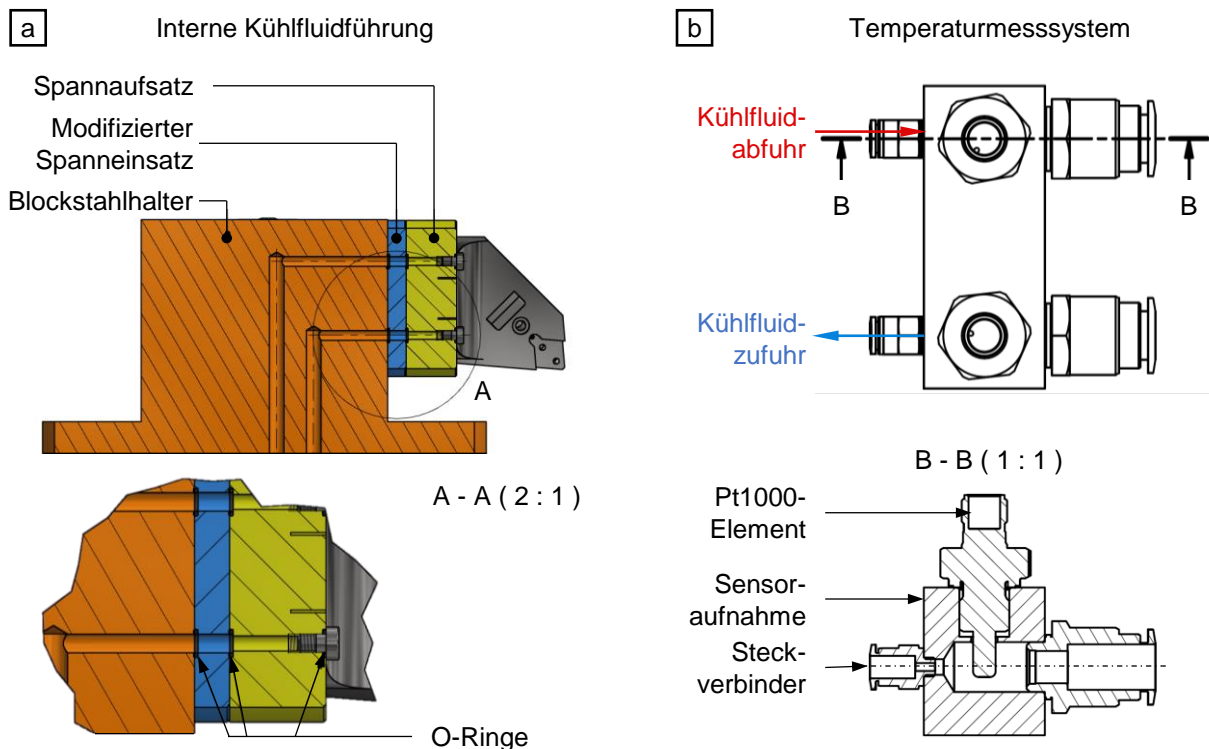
Komponenten des innengekühlten Werkzeugsystems am Blockstahlhalter; a) Werkzeughalter und Kühlleitungen; b) Temperaturmesssystem
